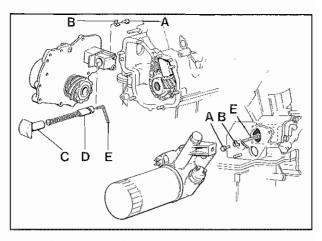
Smontaggio tendicatena Disassembly of chain stratcher
